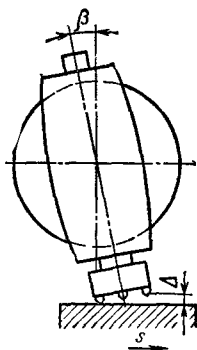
Поворот шпиндельной головки вертикально-фрезерного станка
